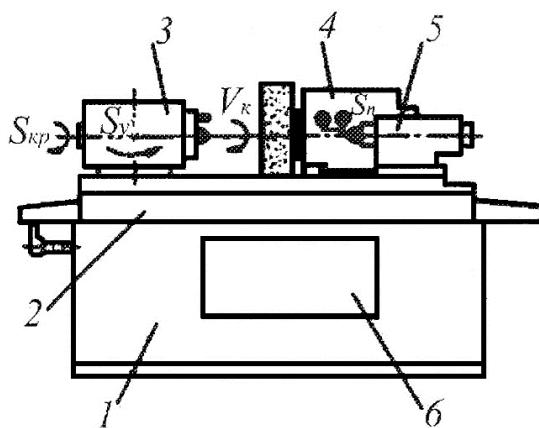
Загальний вигляд круглошліфувального верстата
